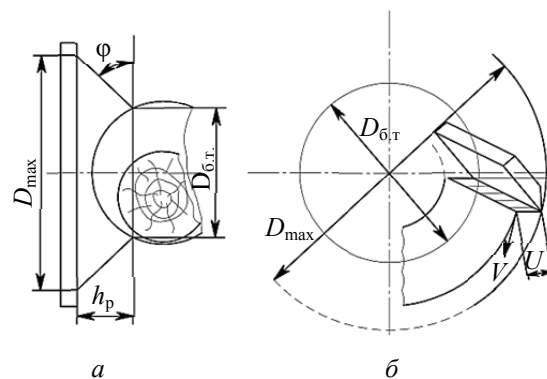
Параметры фрезерования малоножевыми торцово-коническими фрезами:
